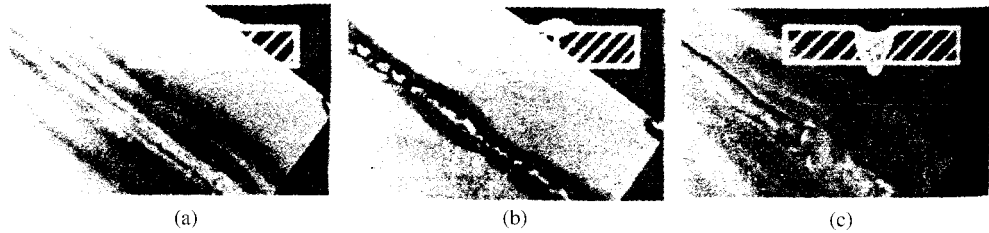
65 焊炬的运动速度与焊缝的形状
